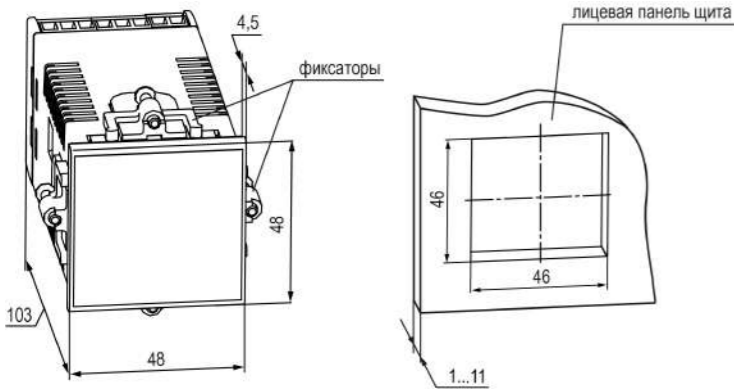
Габаритные размеры корпуса Щ5 и монтажного отверстия в щите
